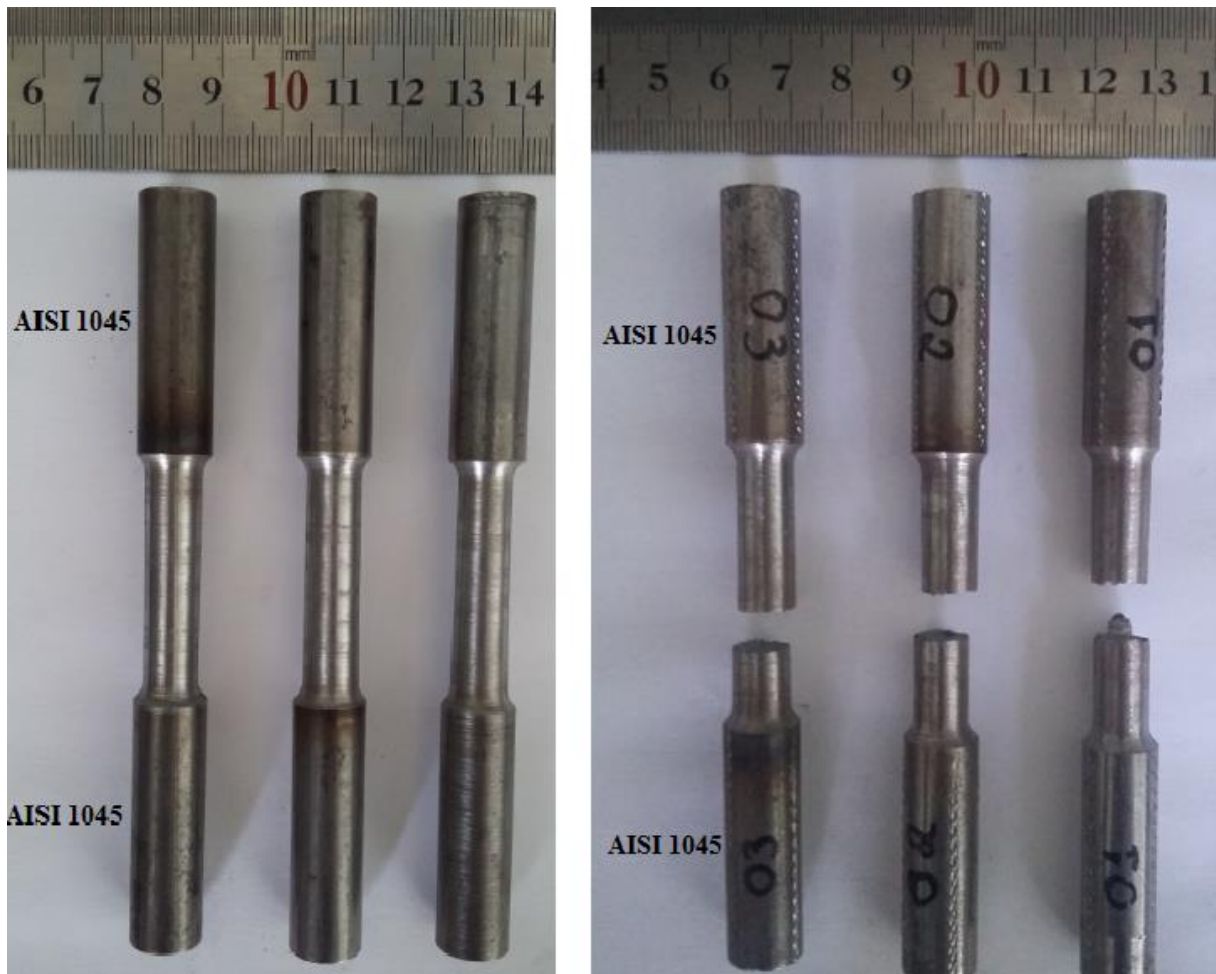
Corpo de prova 26; 3-3-2. Soldagem similar do aço ASTM 1045 e ensaio de tração
